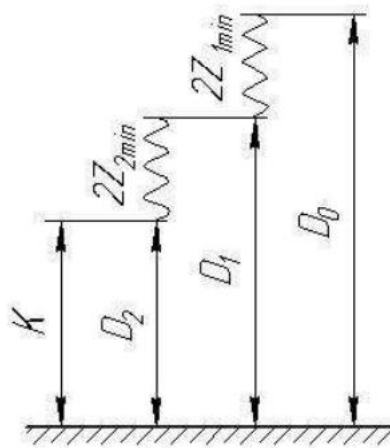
Размерные цепи при обработке наружной поверхности Ø25k7
